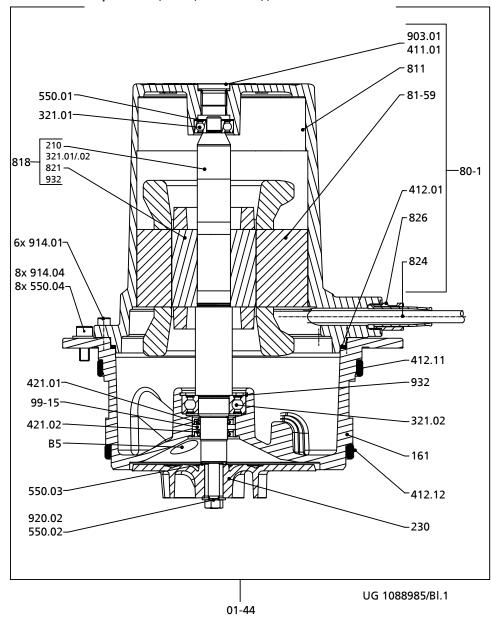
Сборочный чертеж mini-Compacta U60, U100, UZ150 — рабочая часть
